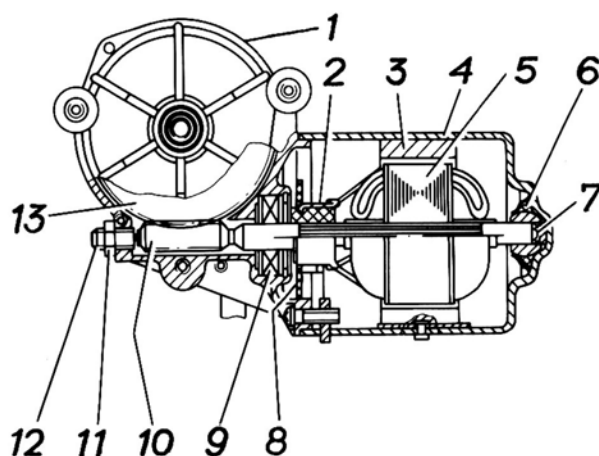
Моторредуктор стеклоочистителя: 1 – корпус редуктора; 2 – коллектор электродвигателя; 3 – магнит; 4 – корпус электродвигателя; 5 – якорь; 6 – подшипник; 7 – упорный шарик; 8 – панель щеткодержателя; 9 – шариковый подшипник; 10 – червяк; 11 – стопорная гайка; 12 – упорный винт; 13 – шестерня
